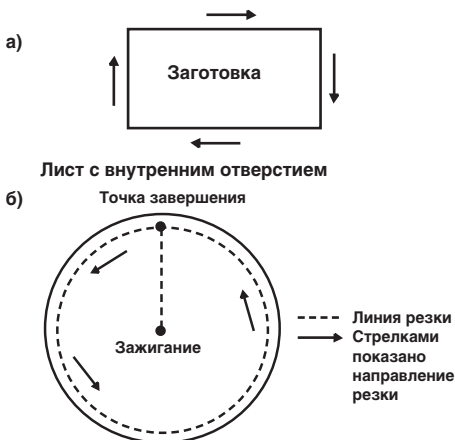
Выбор направления движения обхода: а — для внешнего контура, б — для отверстий
